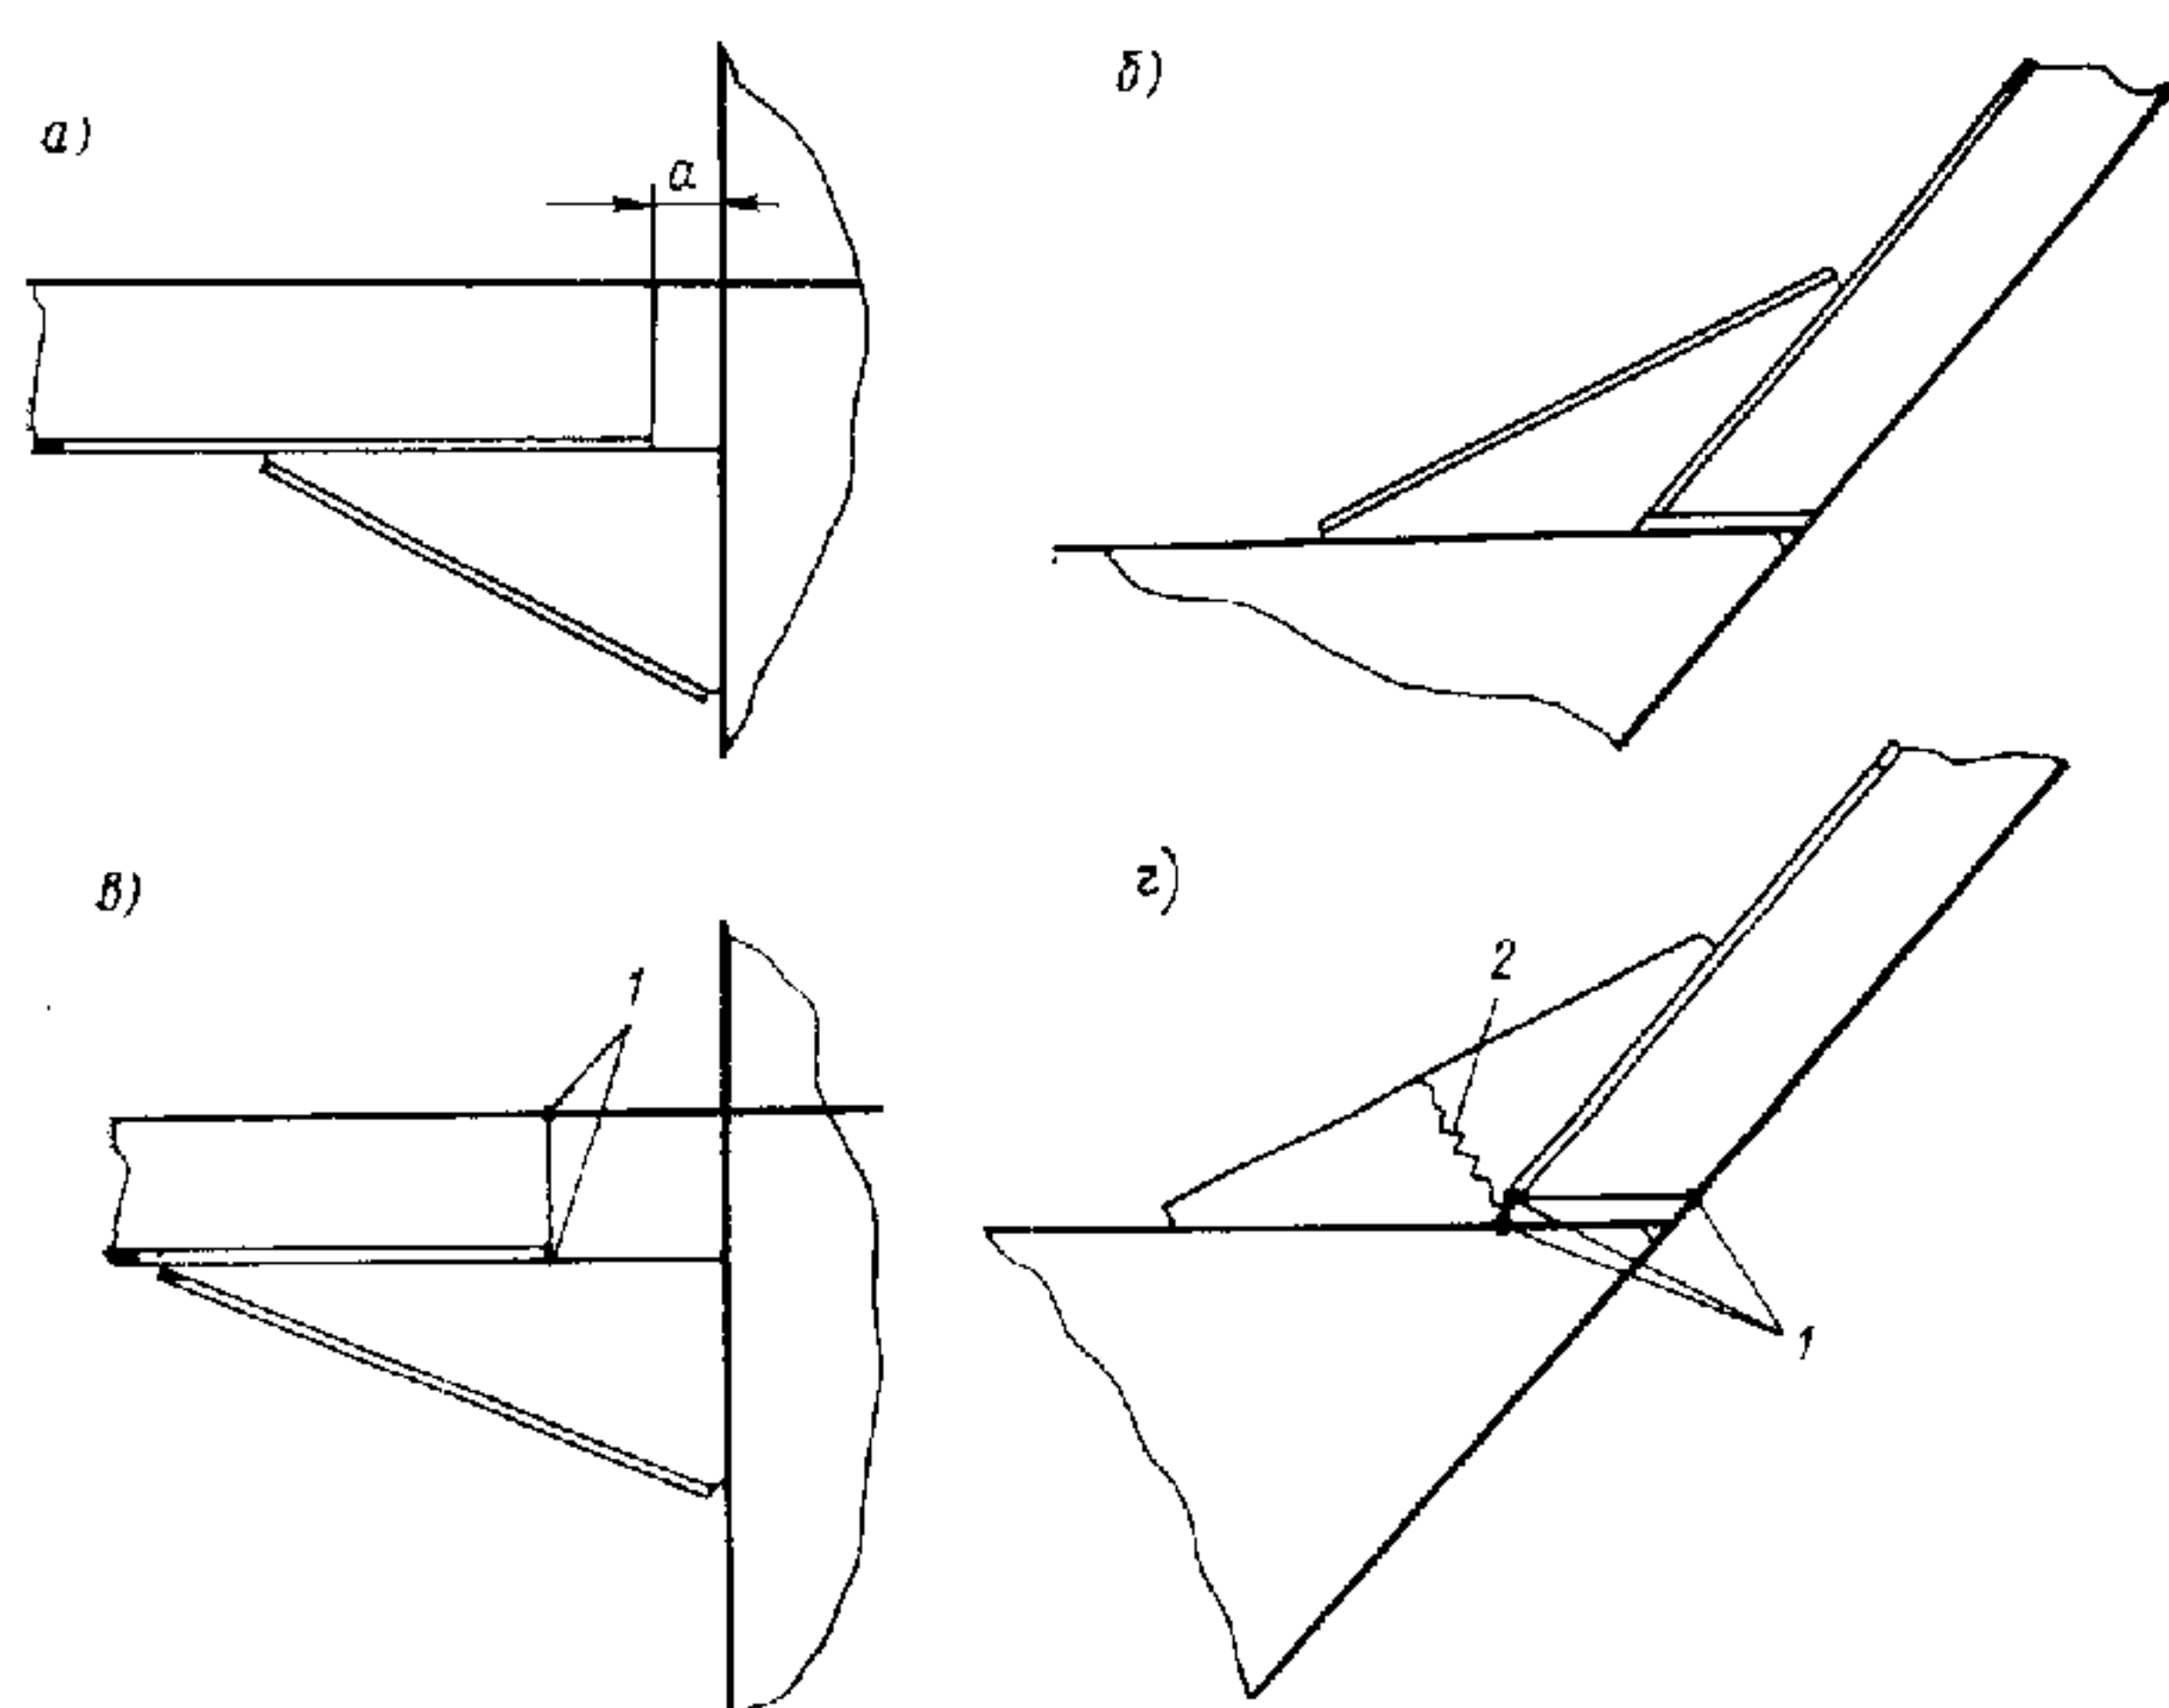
Закрепление кницами концов балок и пиллерсов:
